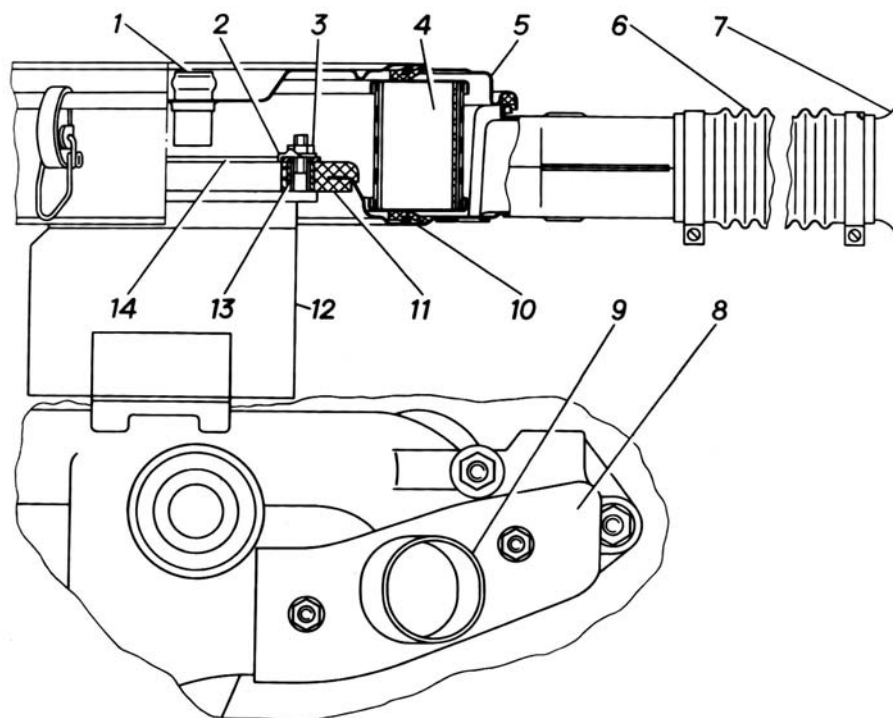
Воздушный фильтр: 1 - патрубок вентиляции картера двигателя; 2 - шайба; 3 - гайка; 4 - фильтрующий элемент; 5 - крышка; 6 - шланг; 7 - заборный патрубок; 8 - экран; 9 - патрубок экрана; 10 - корпус фильтра; 11 - прокладка; 12 - карбюратор; 13 - распорная втулка; 14 - пластина
